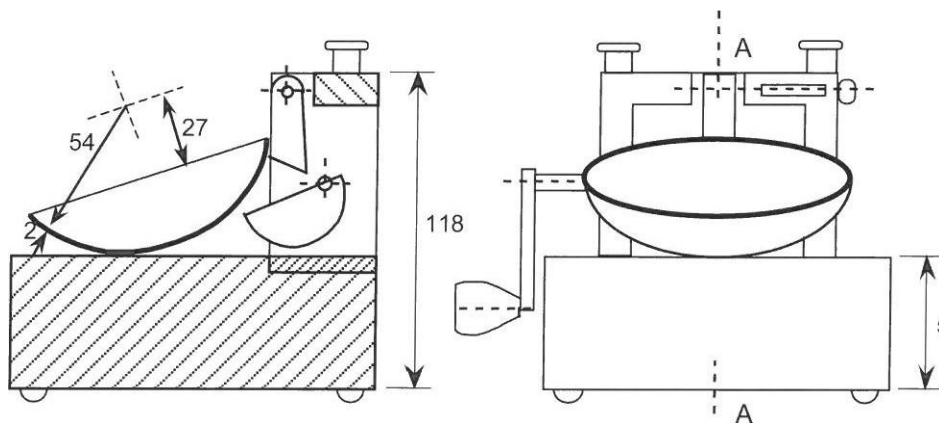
vue de face et coupe droite de l'appareil de CASAGRANDE
